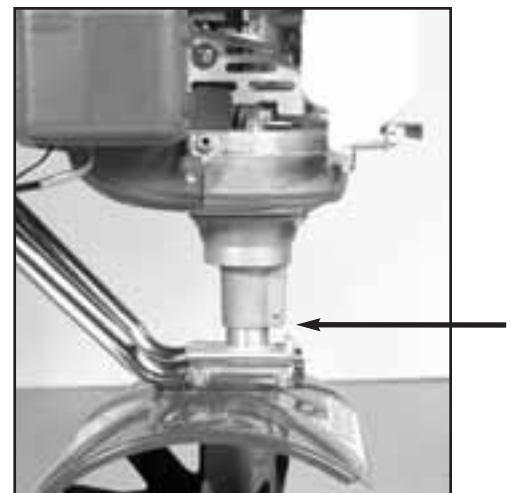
Der Motor liegt nicht richtig auf dem Getriebe auf.
